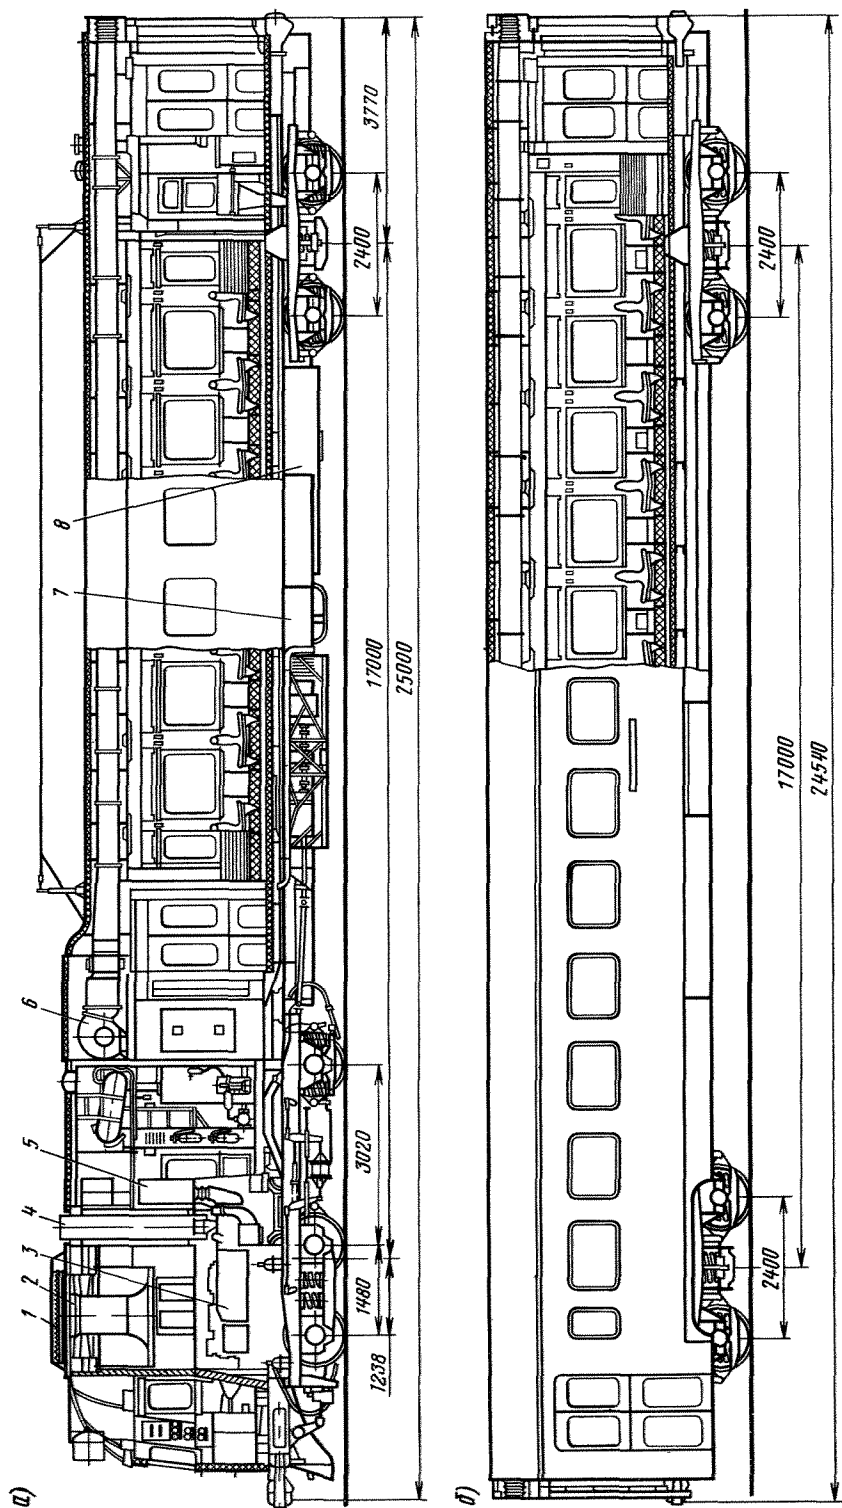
Расположение оборудования и основные размеры моторного (а) и прицепного (б) вагонов дизель поезда Д1
